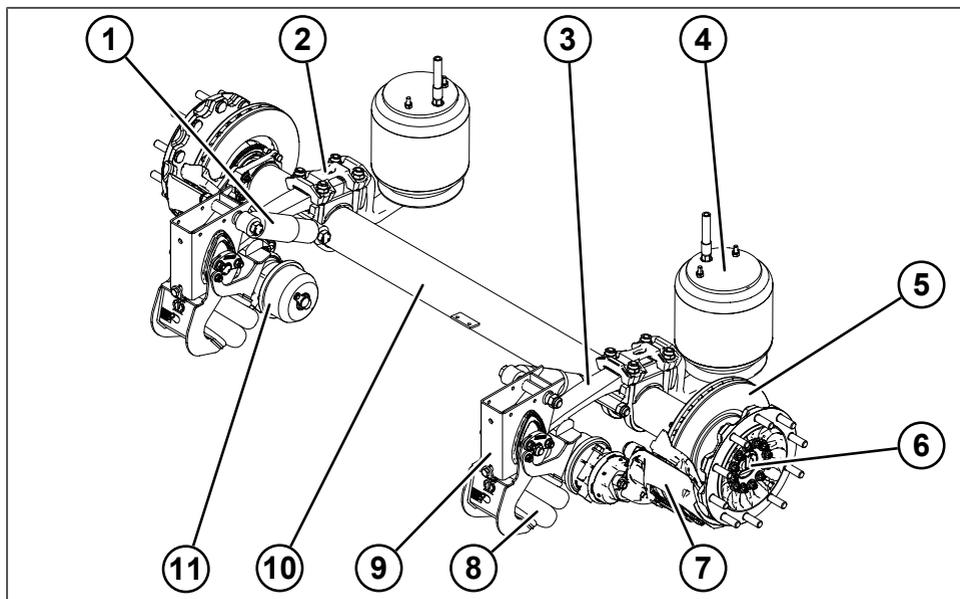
Baugruppen der KRONE Trailer Achse (Luftfederlenker oben)
